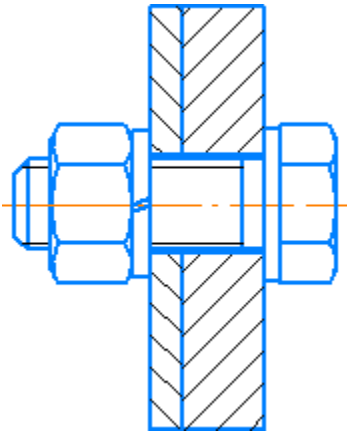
Розрахункова схема болтового з'єднання
